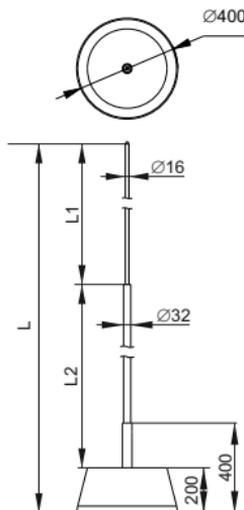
Габаритные размеры комплекта (4 м) / Figure 2 – Overall dimensions of the kit (4 m)
